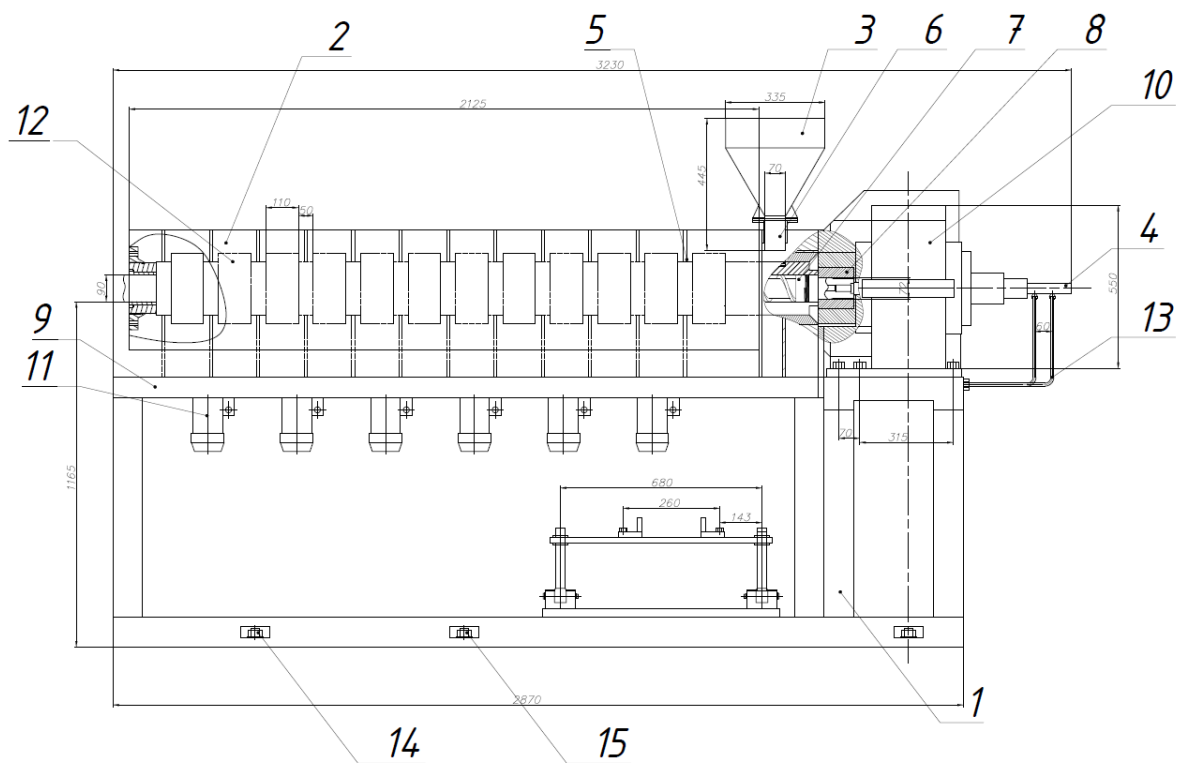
Черв'ячний екструдер для виготовлення труб:
